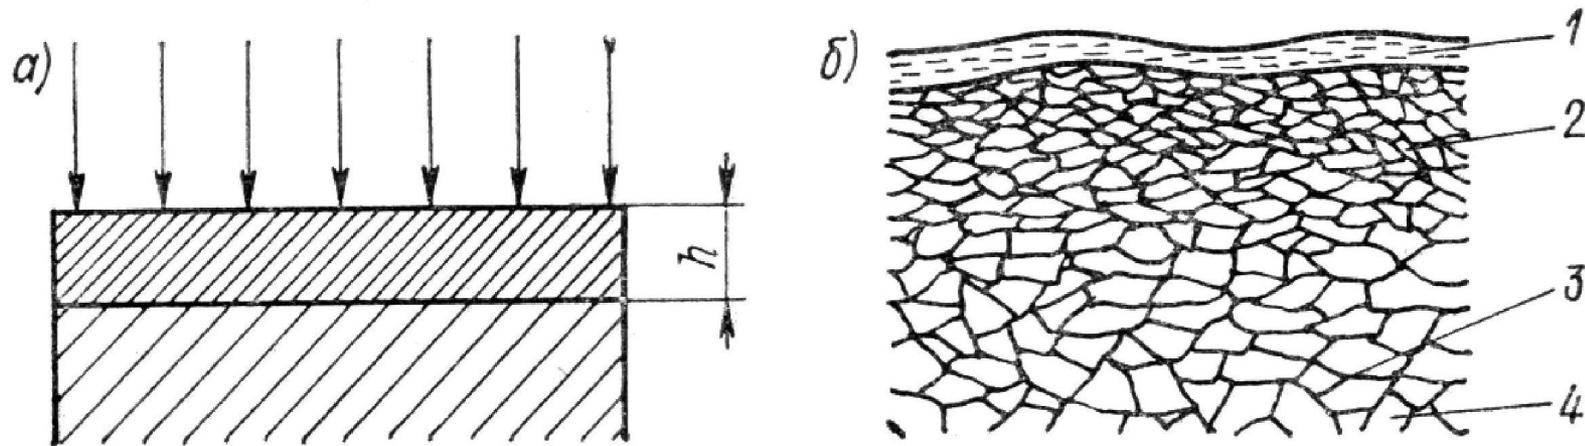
Схема механической обработки заготовки детали (а), строение поверхностного слоя детали после механической обработки (б)
